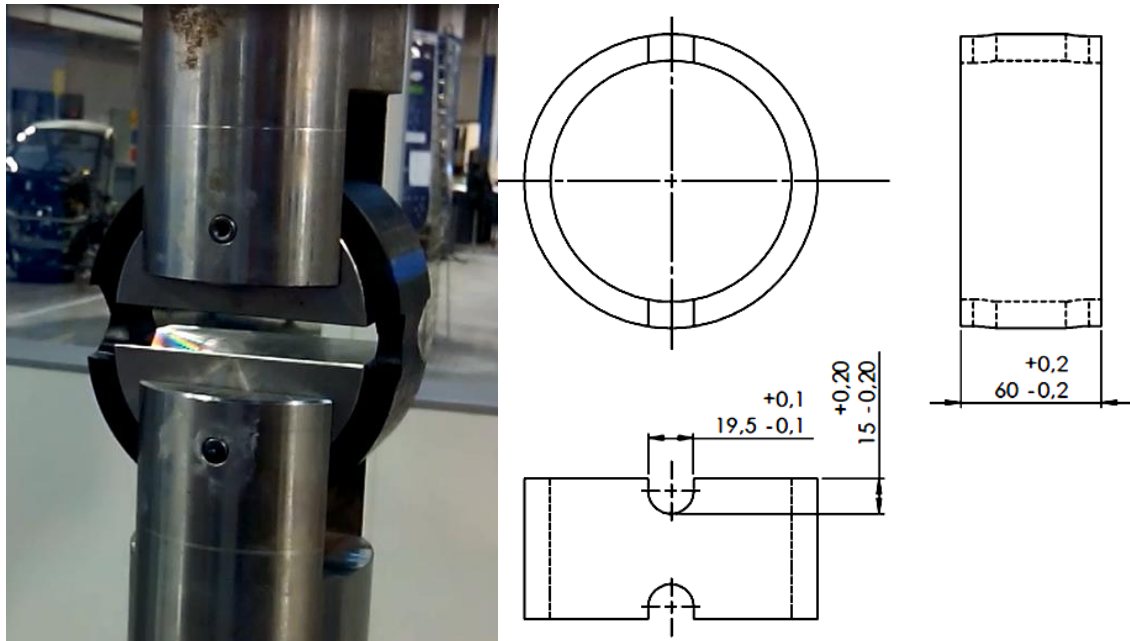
Dispositif de pré-hension et géométrie de l'éprouvette
